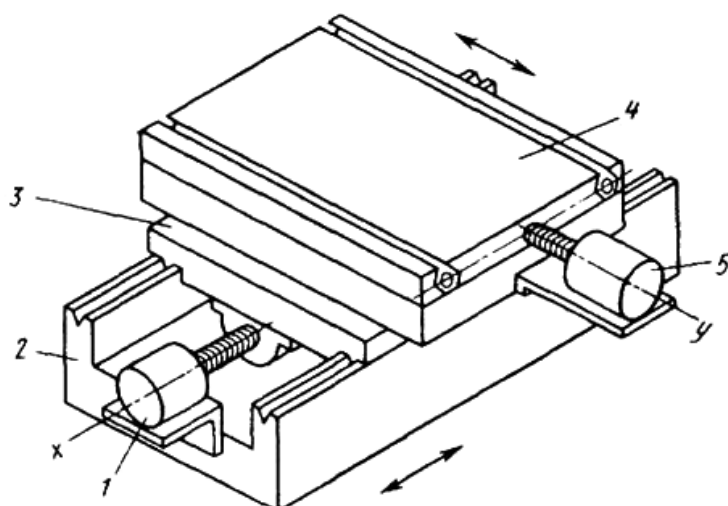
Схема конструкции двухкоординатного стола: 1 – привод нижней каретки; 2 – основание; 3 – нижняя каретка; 4 – верхняя каретка; 5 – привод верхней каретки
